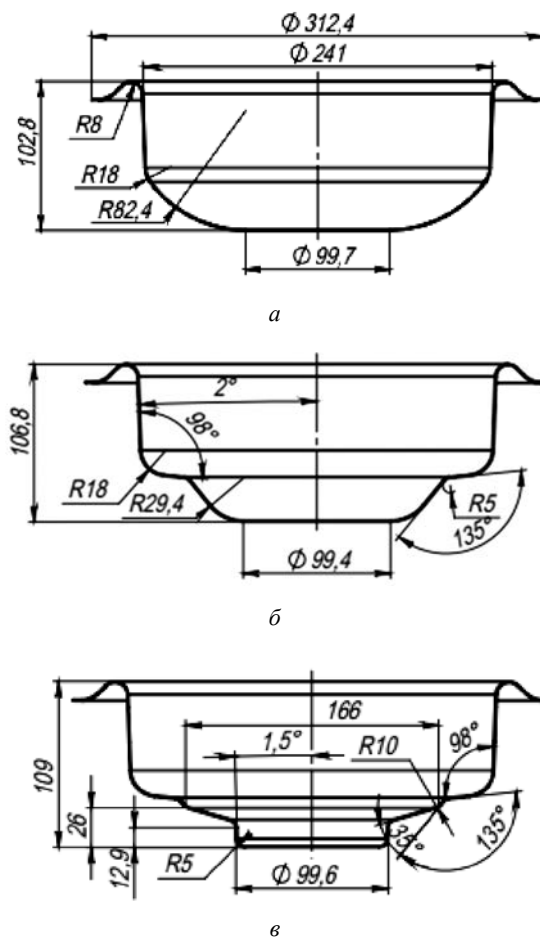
Технологічні переходи виготовлення напівфабрикату корпусу вентилятора: а – перша витяжка; б – друга витяжка; в – третя витяжка
